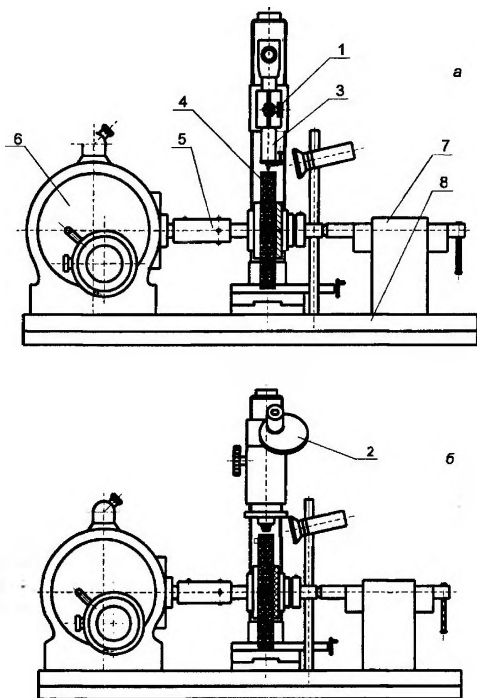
Установка для изучения разбавления зерен на рабочей поверхности круга
